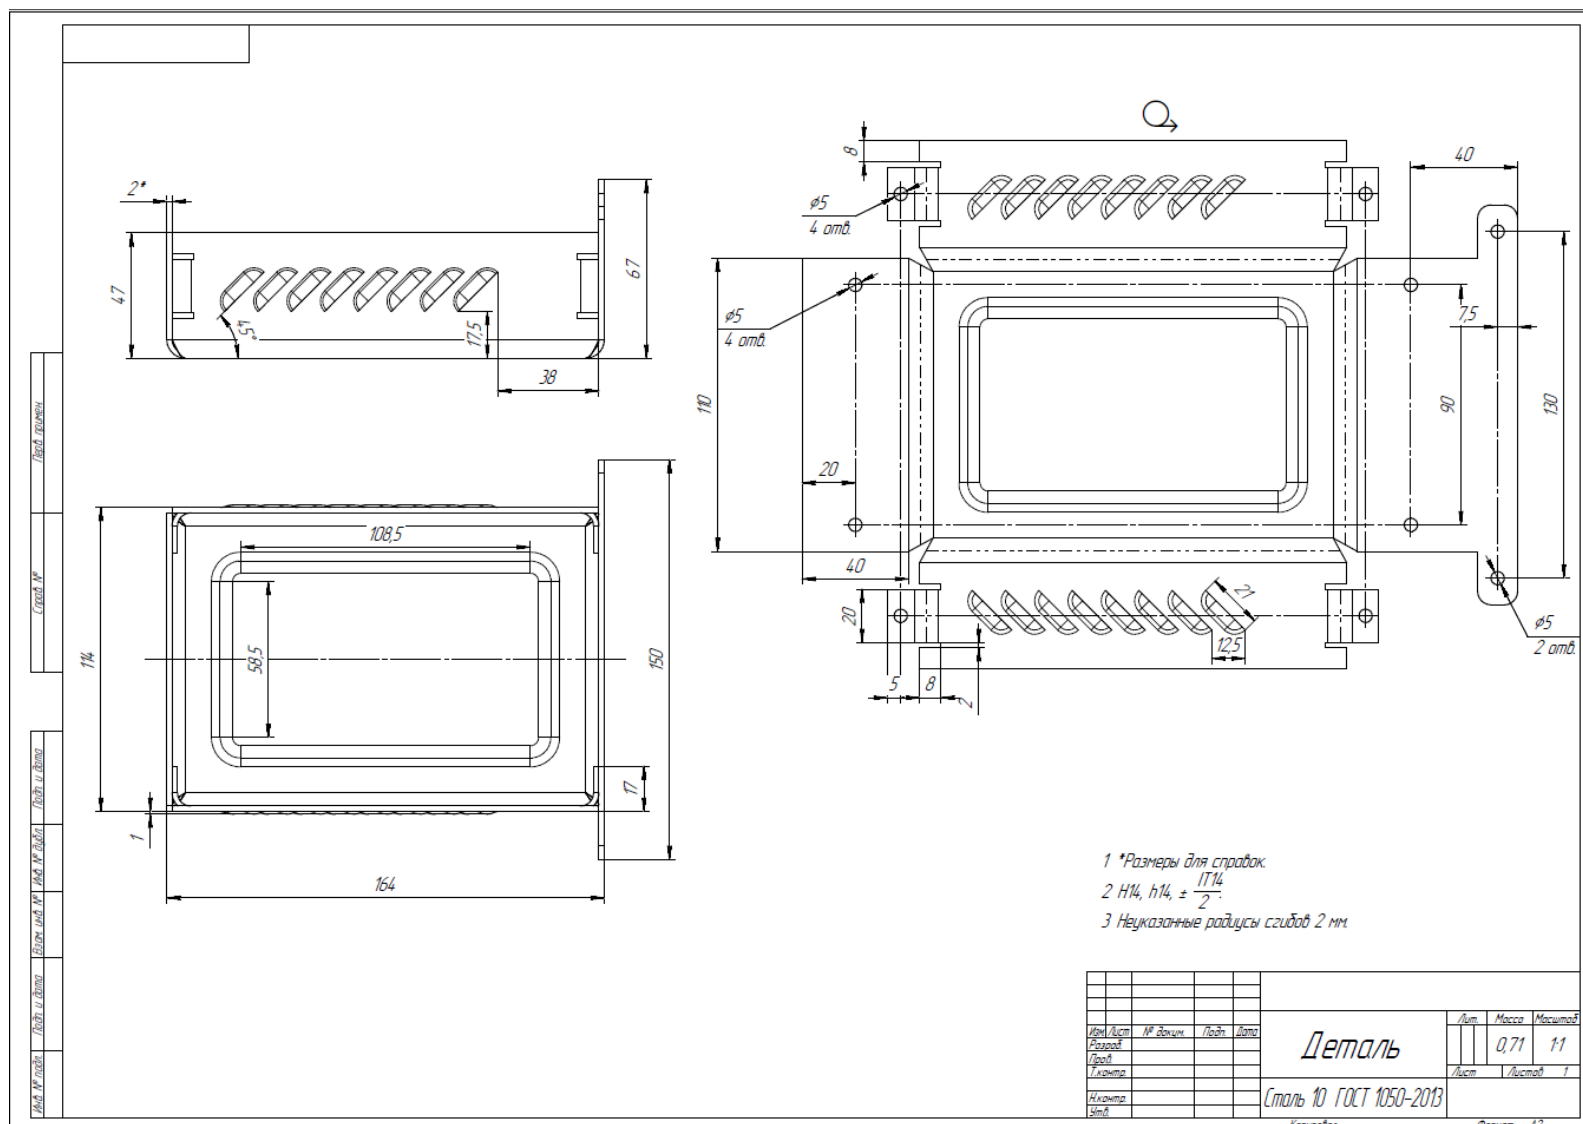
Чертеж детали «Корпус» (вариант 2)
